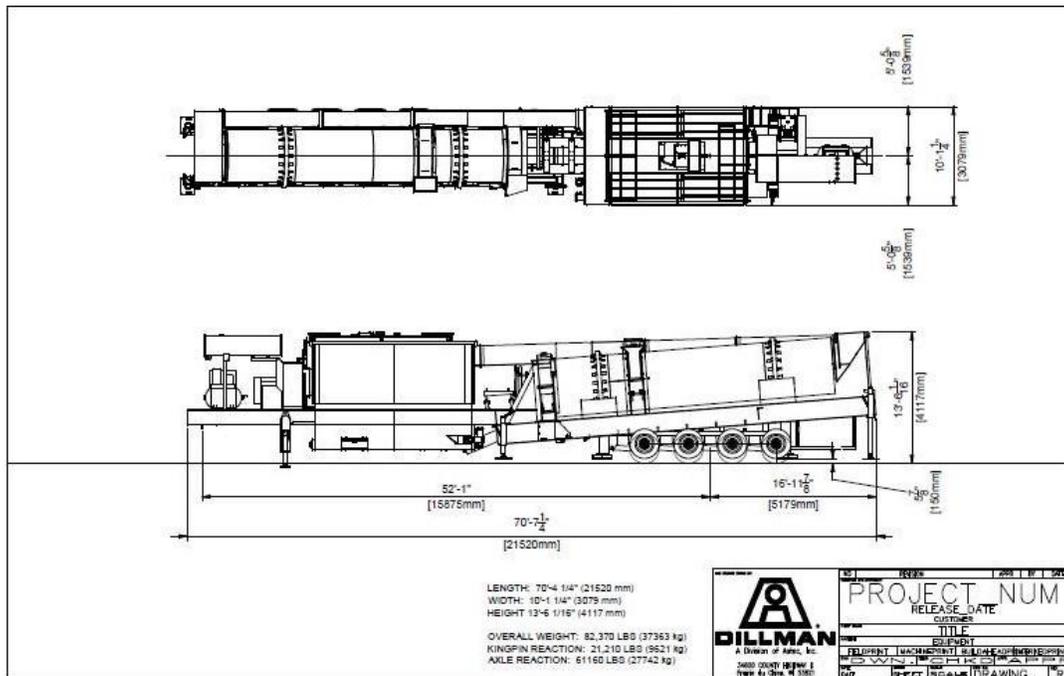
Dimensiones de Planta de Asfalto Voyager 120.
